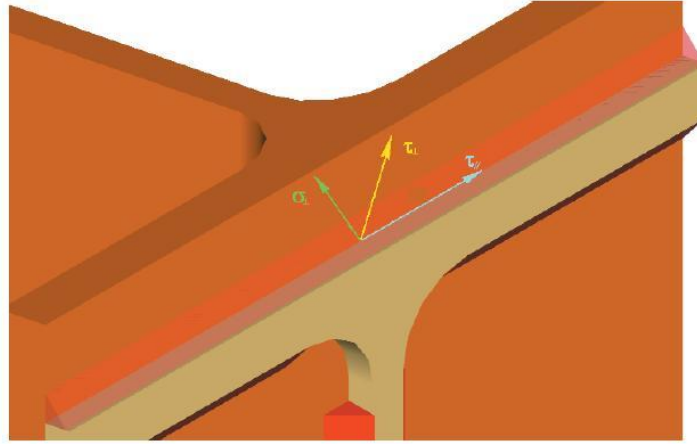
Descomposición de los esfuerzos transmitidos al cordón de soldadura.
